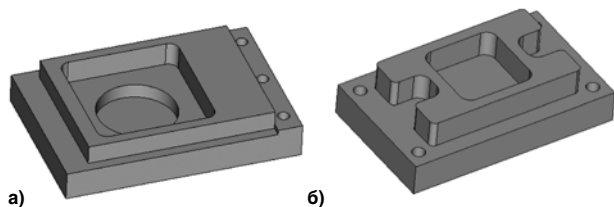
3D-модели парного изготовления деталей: а) первая деталь; б) вторая деталь
